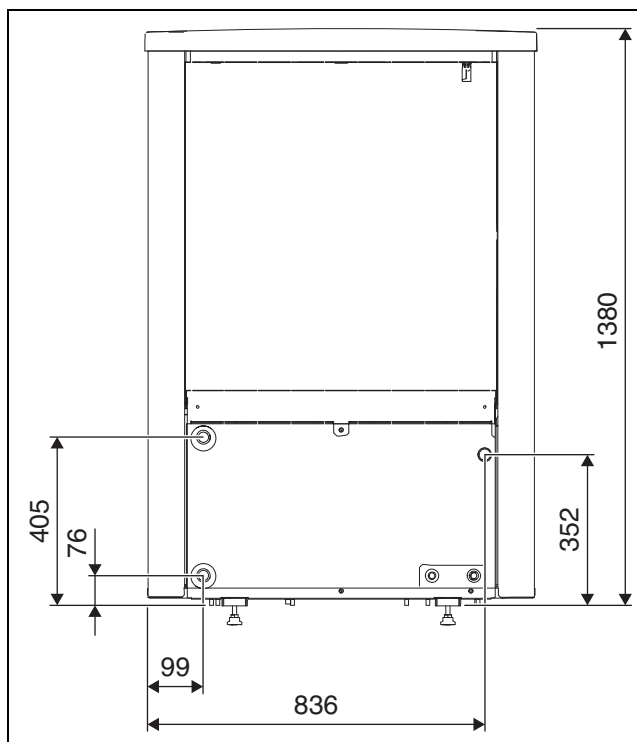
Dimensioni e attacchi del modello di pompa di calore 5-9, lato posteriore
